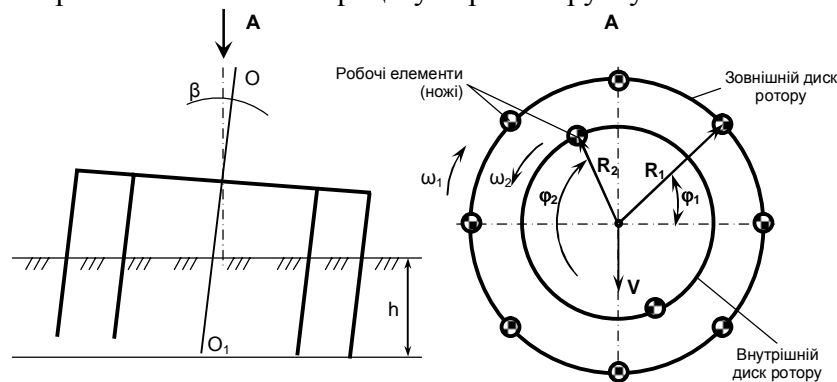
Конструктивно-технологічна схема вертикально-фрезерного адаптера
